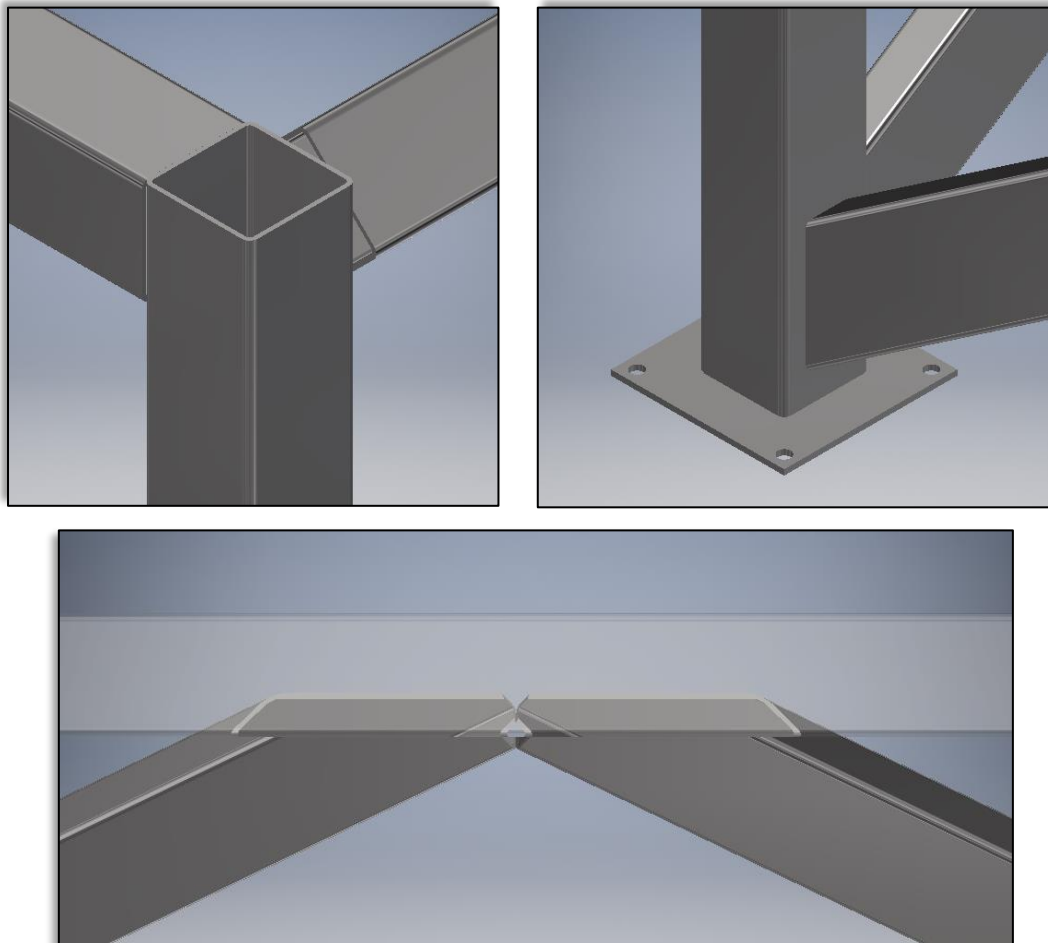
Extremos de caños para soldadura según ángulos y posición
